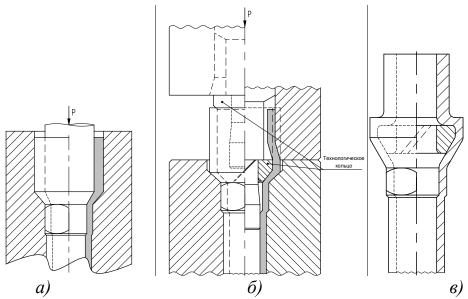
Схема формообразования полуфабриката на четвертом переходе штамповки (а), схема установки технологического кольца А в полуфабрикат (б) и головка насосной штанги после последнего перехода штамповки (в)
